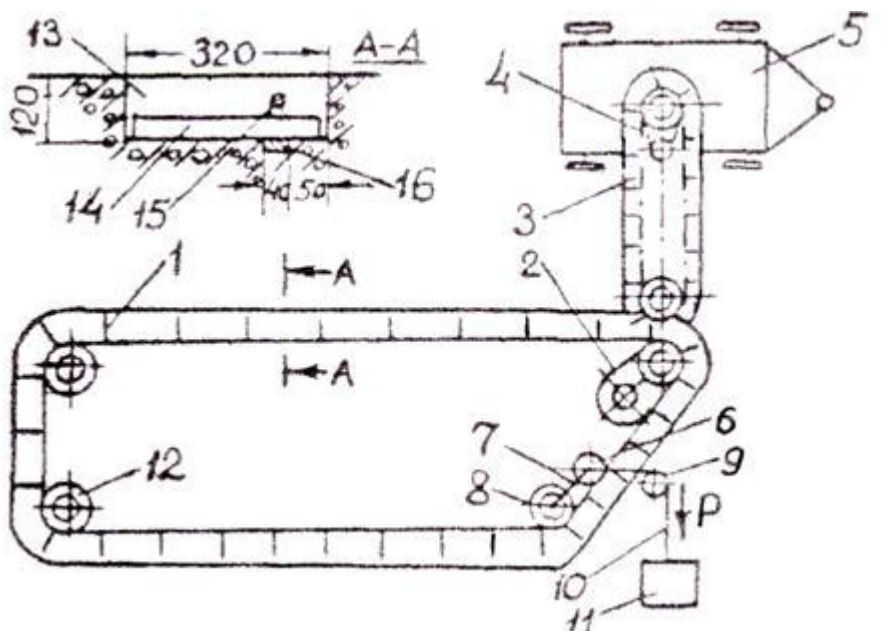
Схема навозоуборочного транспортера ТСН-160А:
